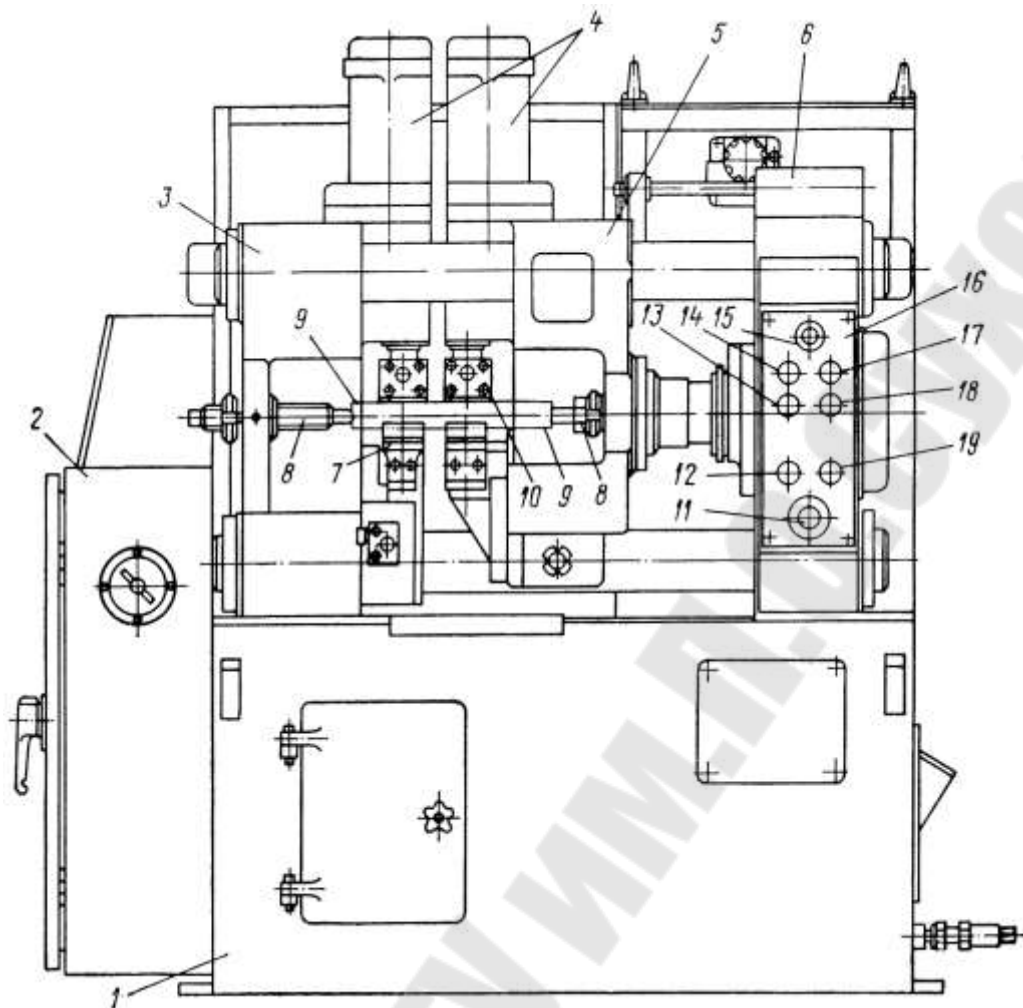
Эскиз общего вида сварочного полуавтомата модели СА-2: 1 – станина; 2 – шкаф электрооборудования; 3, 6 – левая и правая стойки; 4 – цилиндр зажима заготовок; 5 – каретка; 7, 10 – неподвижные и подвижные призмы; 8 – упоры; 9 – свариваемые заготовки; 11 – регулятор реле напряжения для отвода каретки; 12 – переключатель режима работы; 13 – кнопка «←→»; 14 – кнопка «Пуск»; 15 – лампочка «Напряжение»; 16 – панель управления; 17 – кнопка «Стоп»; 18 – кнопка «←»; 19 – кнопка «Зажим–отжим»
